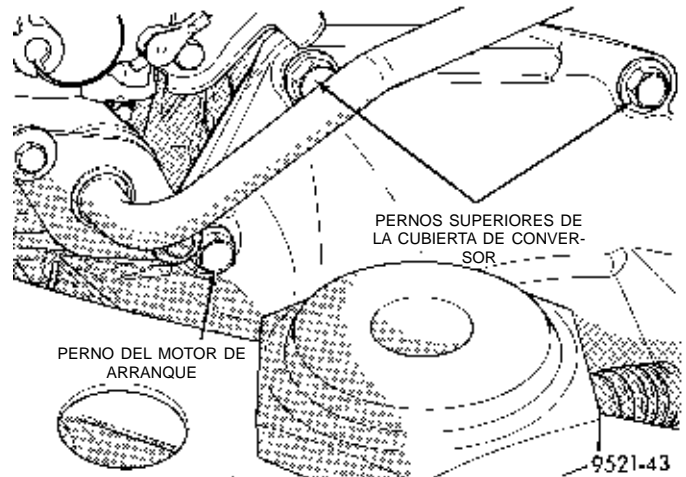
Pernos del motor de arranque y de la cubierta del convertidor
